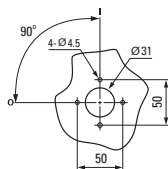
г – Монтажные размеры при установке на дверцу шкафа для рубильников 400-630 А
